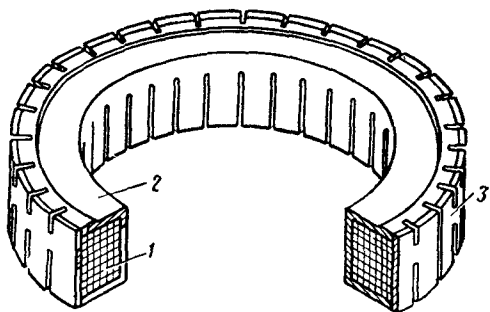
Кольцевой индукционный нагреватель для распайки обмоток якоря в петушках коллектора:
